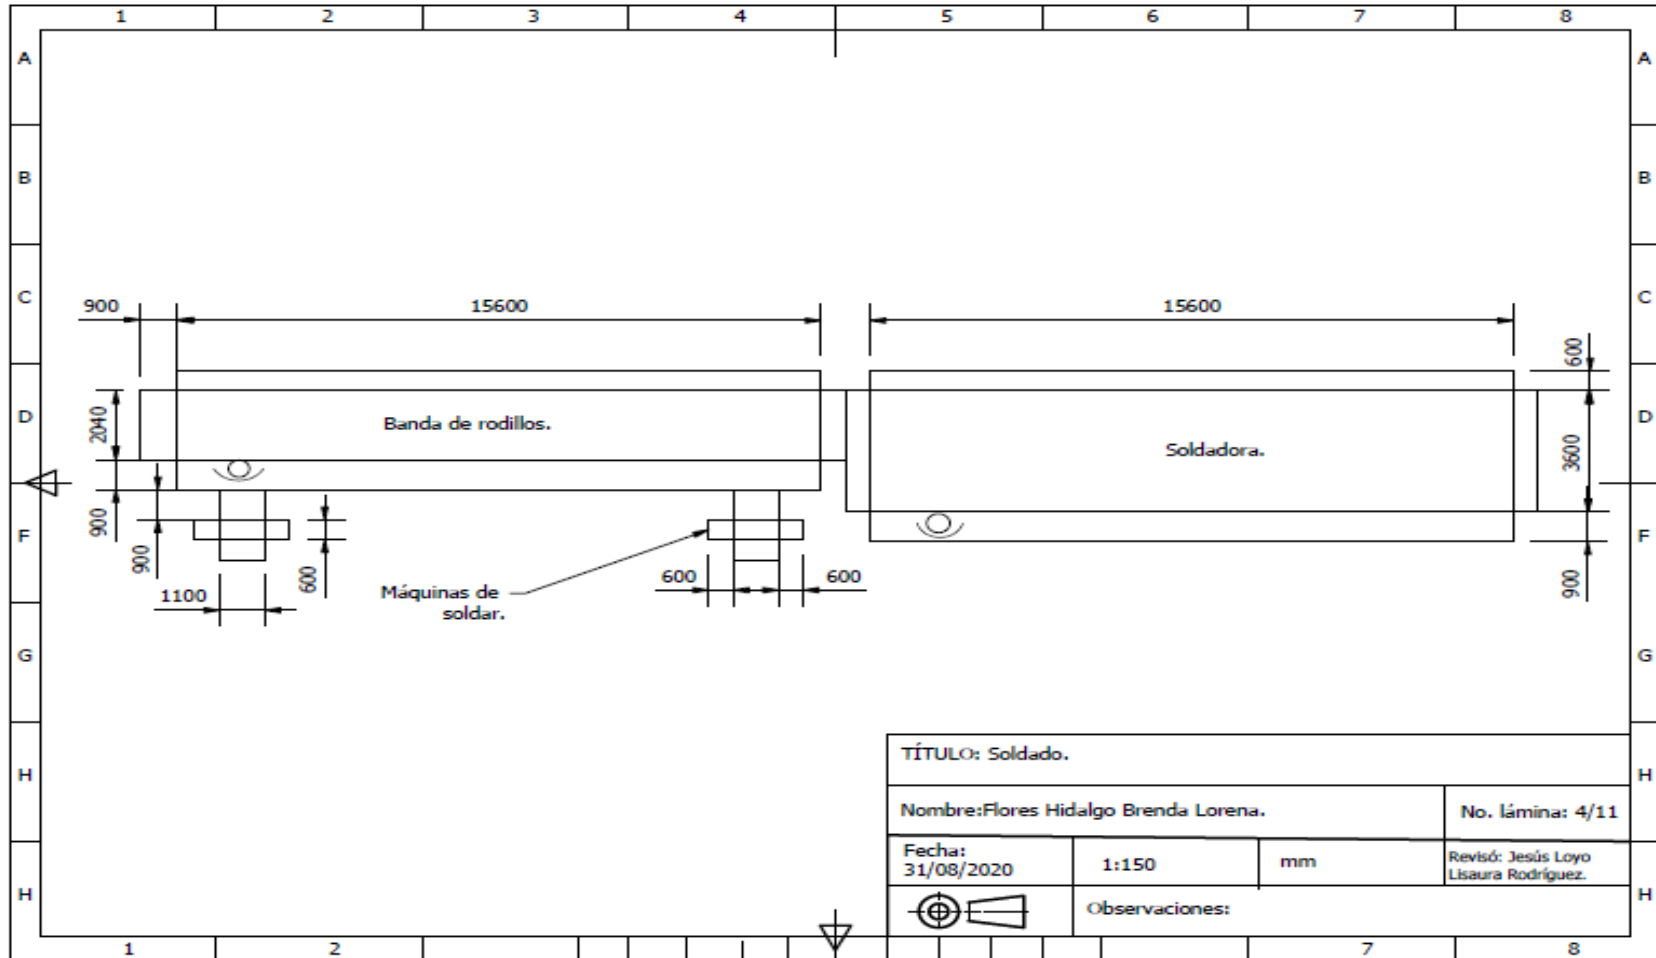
Plano del espacio requerido para la estación de subensambles (soldado). Fuente: Elaboración propia.
